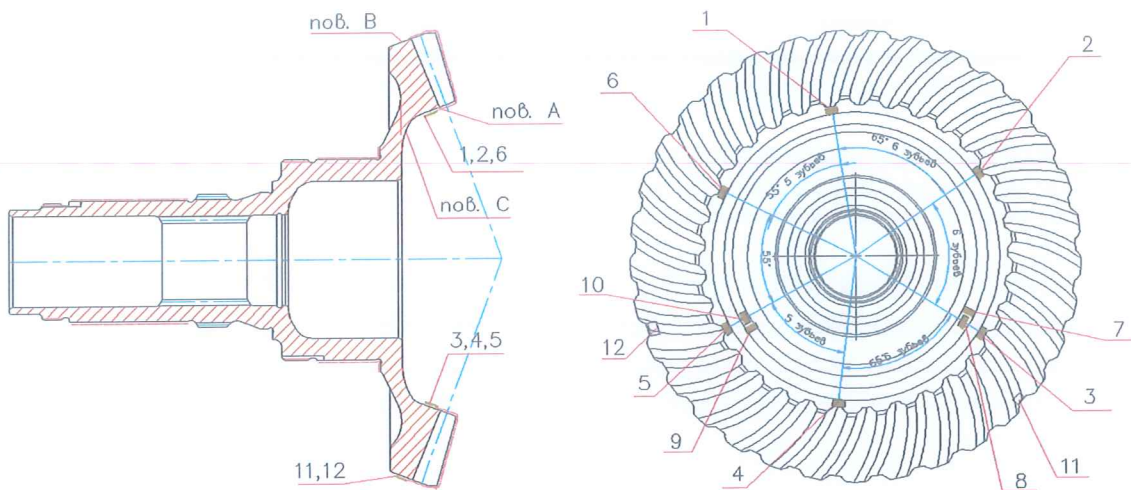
Зубчатое колесо с круговым зубом главного редуктора вертолета, препарированное тензорезисторами для контроля переменных напряжений
